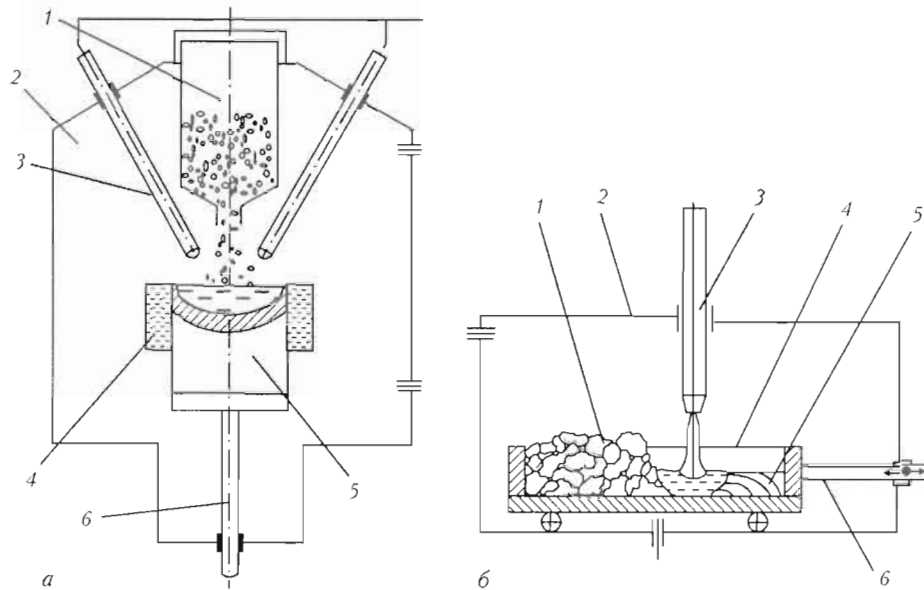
Схемы установок УПП-3 (а) и ОБ1957 (б): 1 — шихта; 2 — плавильная камера; 3 — плазмотрон; 4 — кристаллизатор; 5 — слиток; 6 — механизм вытягивания слитка
